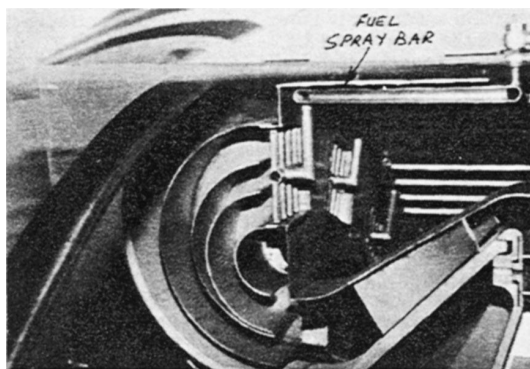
Úspořádání leteckého motoru HeS 3B [10]
